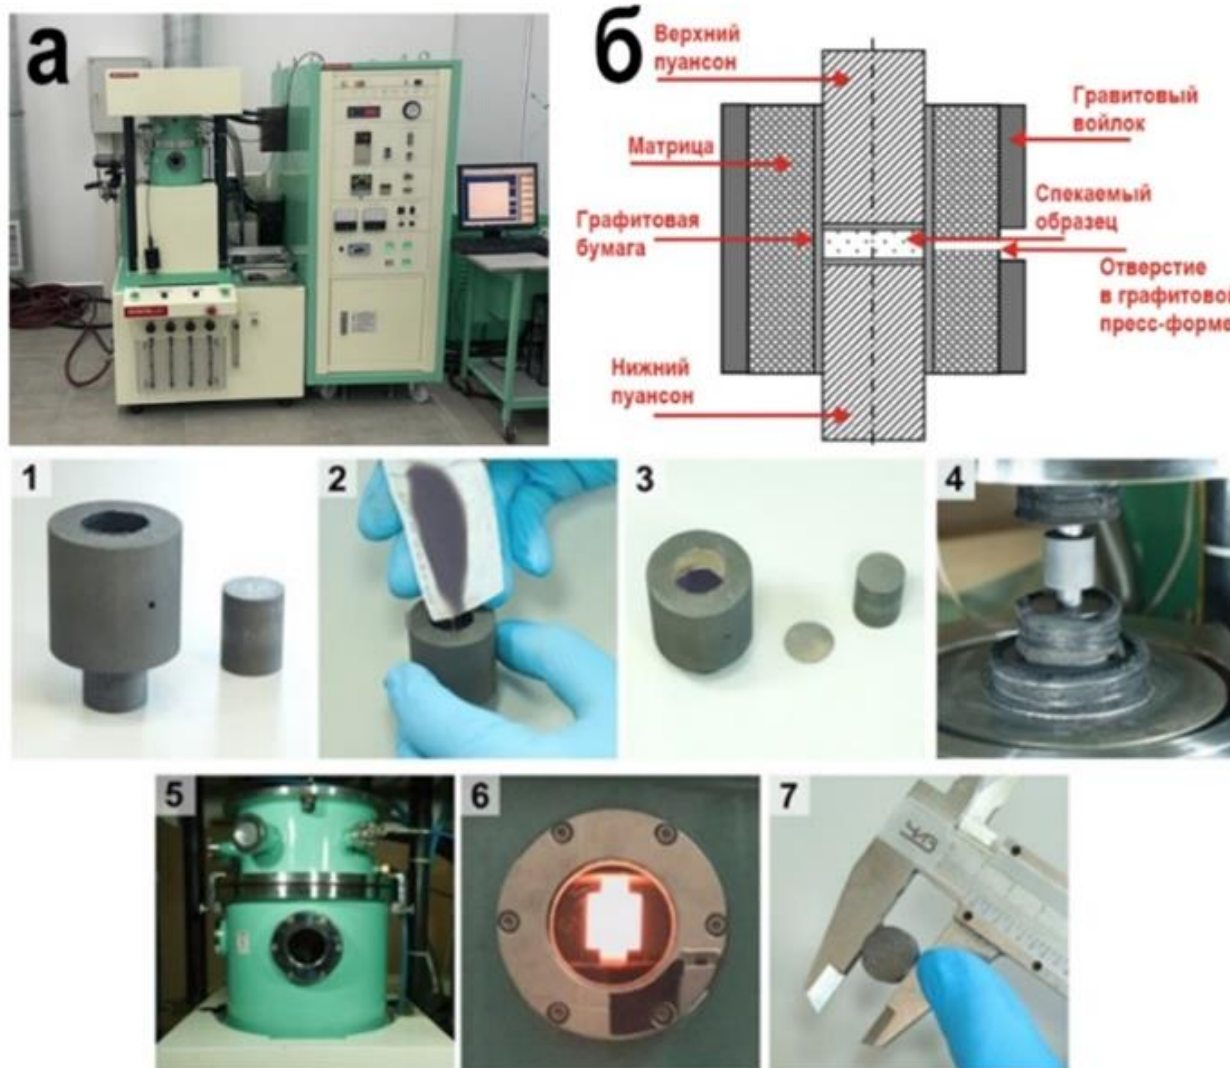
Установка SPS-515S «Dr.Sinter LAB™»: а – общий вид установки; б – схематическое изображение графитовой пресс-формы. Стадии ИПС получения образцов ТС: 1–3 – засыпка стартового порошка композиционной смеси в графитовую пресс-форму, 4 – подпрессовка порошка и установка пресс-формы в камеру спекания, 5 – вакуумирование камеры спекания, 6 – спекание, 7 – полученный образец ТС.
